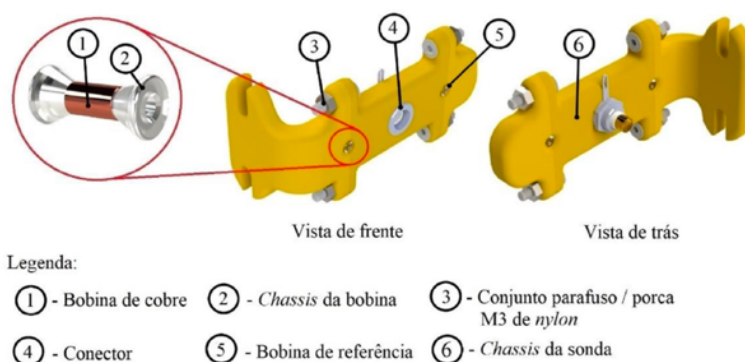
Sonda do Fio de soldadura e chassi das bobinas [82].
